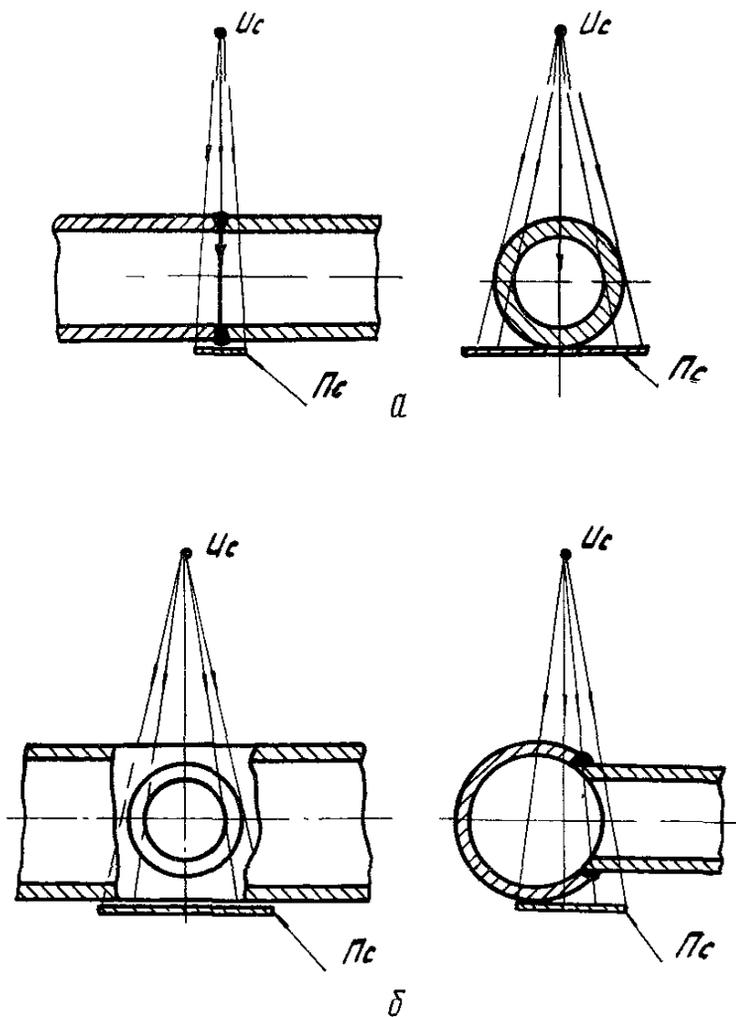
Схема фронтального просвечивания через две стенки за одну установку источника излучения без его смещения относительно сварного шва: а - для соединения труб; б - для соединения врезок
